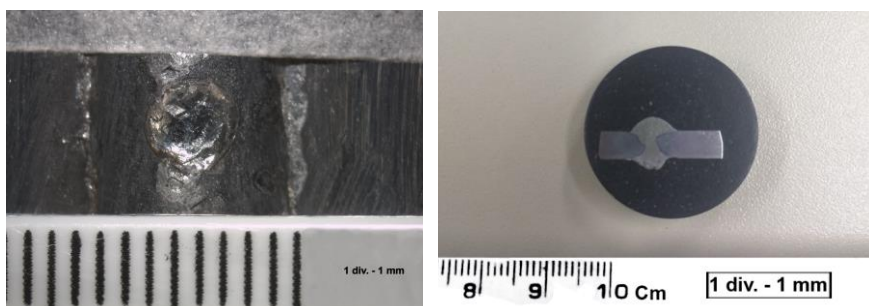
Detalhe superfície e perfil do cordão de solda do corpo de prova 4.
